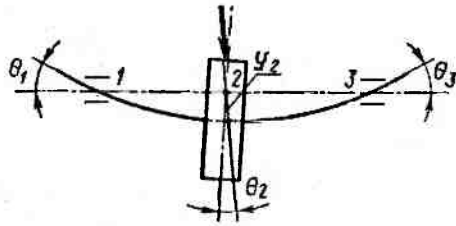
Прогiby валов и повороты их сечений под зубчатыми колесами и в подшипниках
